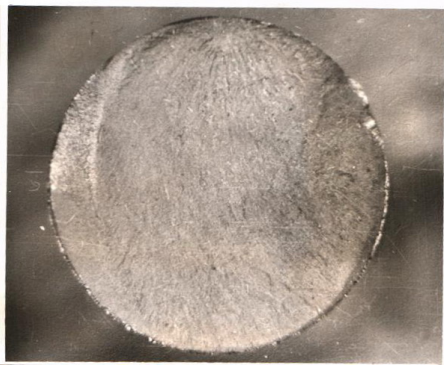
Усталостный излом упрочненного образца из сплава ВТ9
